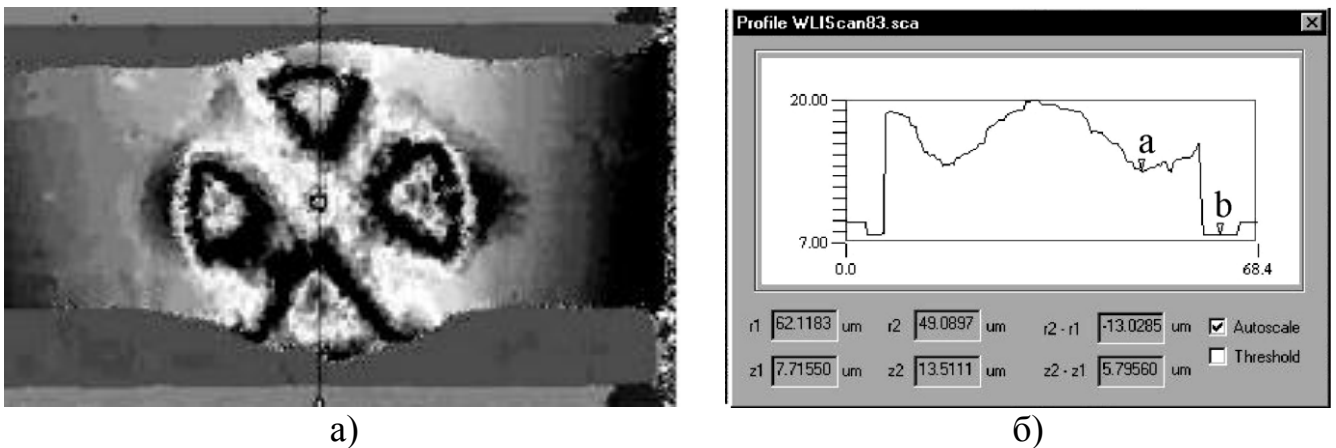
Зварне з'єднання (а) та профіль зварного з'єднання (б)
